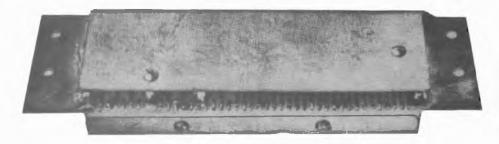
Montaggio ultimato visto dal lato piste, protetto dall'apposito schermo.
